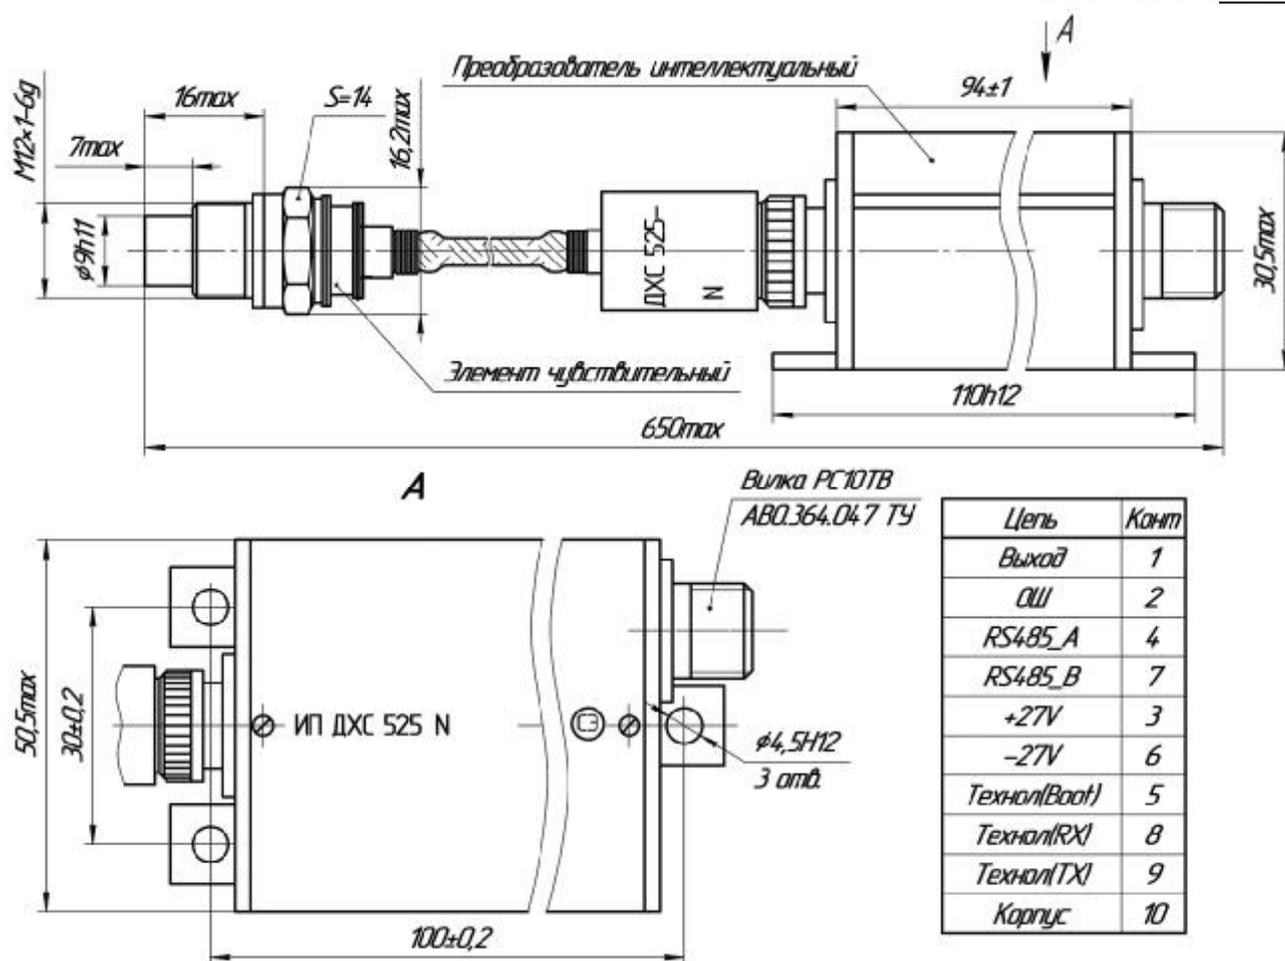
Габаритно-установочные размеры датчика ДХС 525
